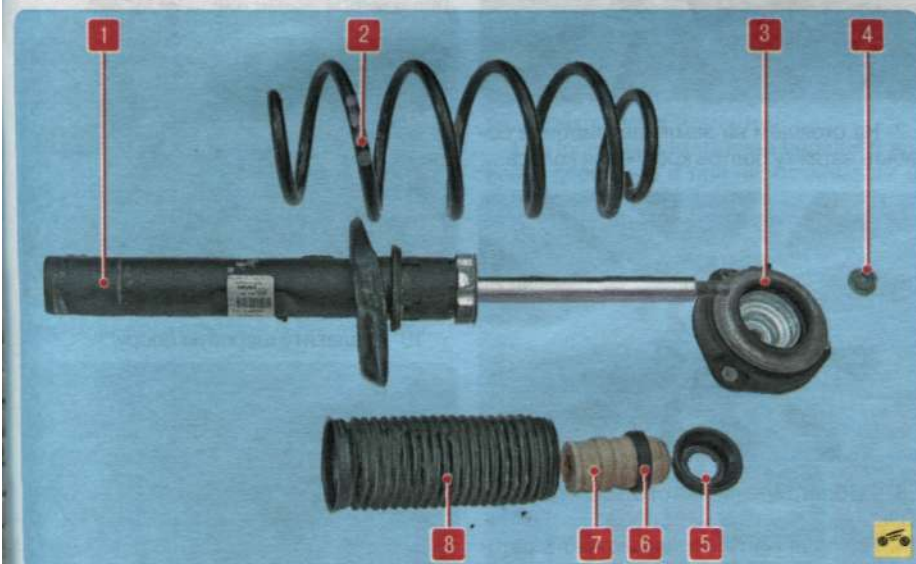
Детали амортизаторной стойки: 1 - амортизатор; 2 - пружина; 3 - верхняя опора; 4 - гайка штока амортизатора; 5 - защитный колпачок; 6 - стопорное кольцо кожуха; 7 - буфер хода сжатия; 8 - защитный кожух
